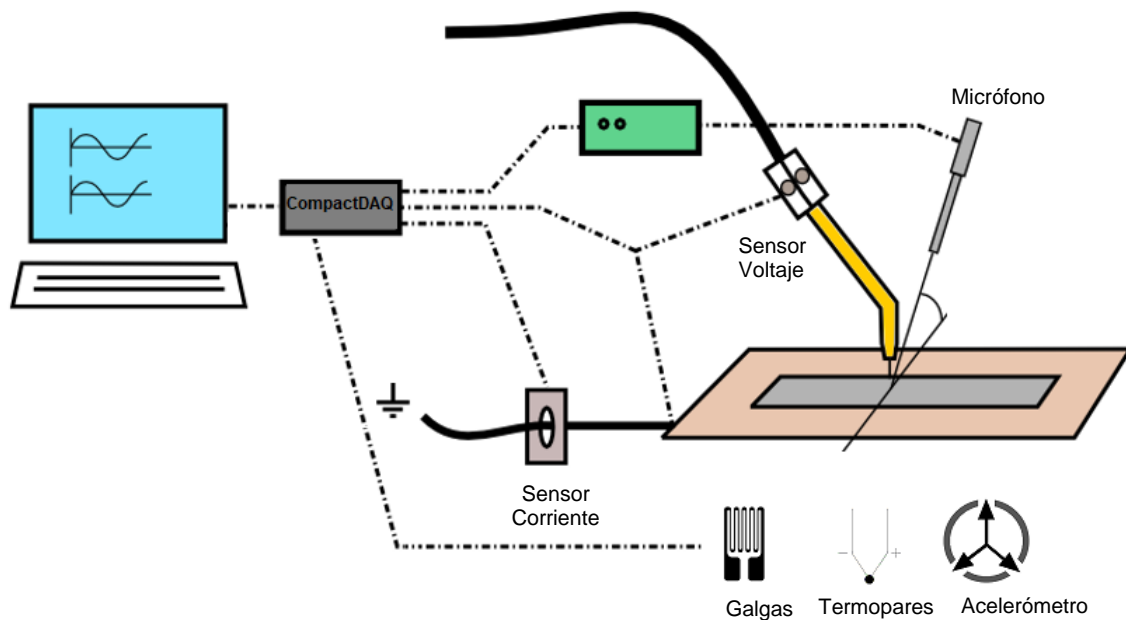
Diseño de la instrumentalización de los cupones de soldadura
